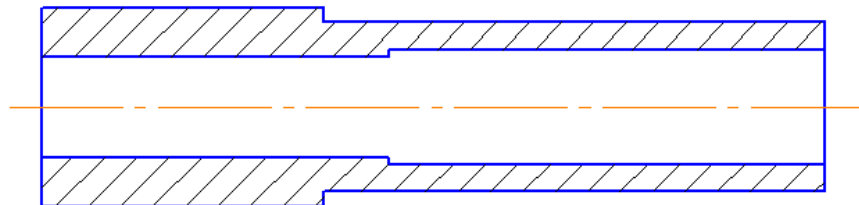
креслення заготовки деталі «Корпус»
